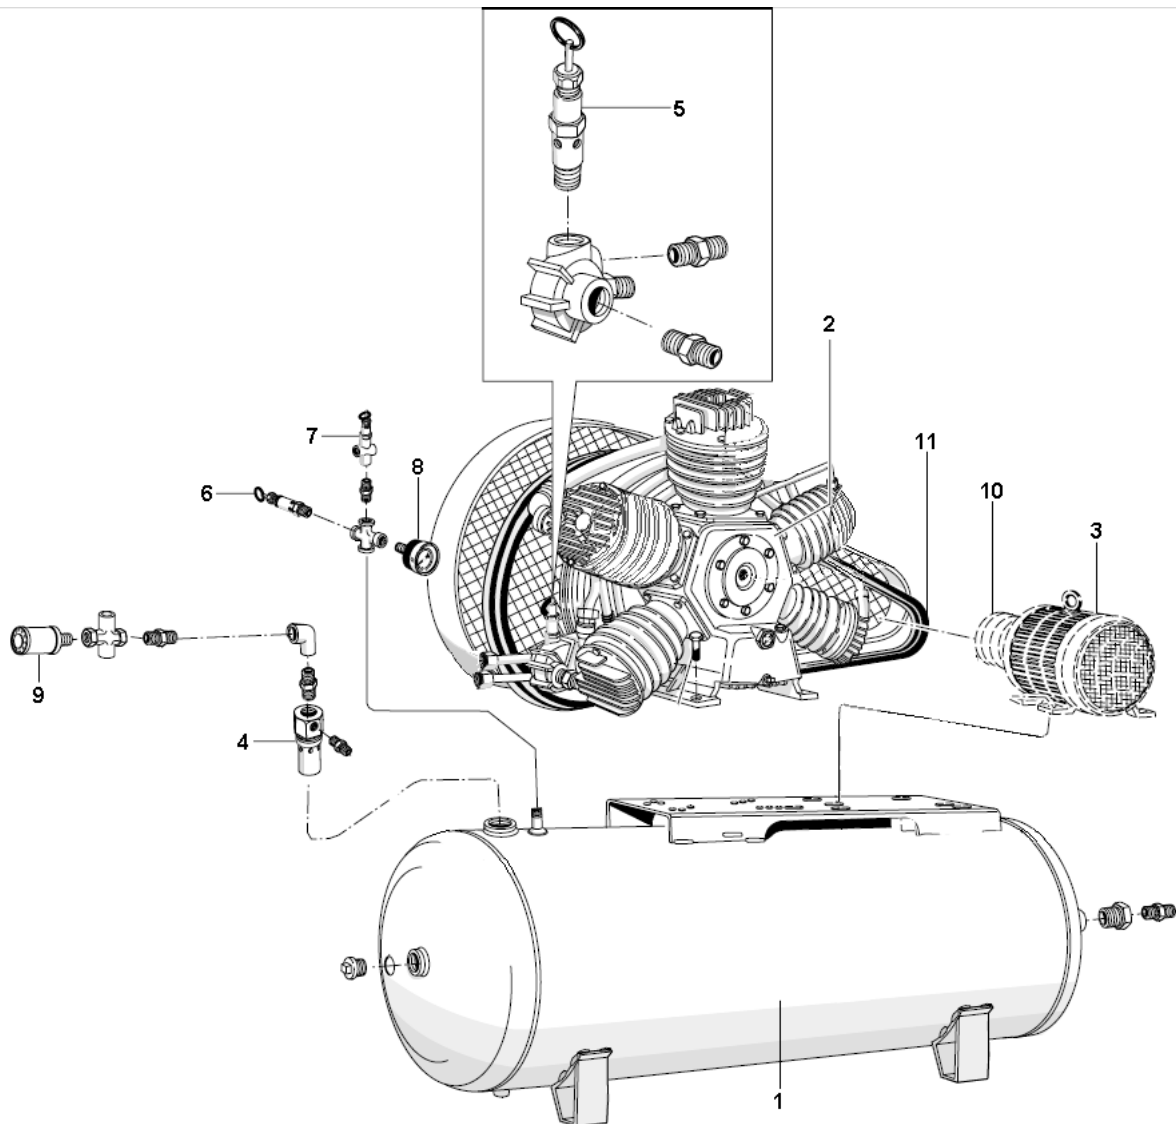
Compressor de ar / Compresora de aire / Air compressor / Compresseur à air 80/100 PCM
